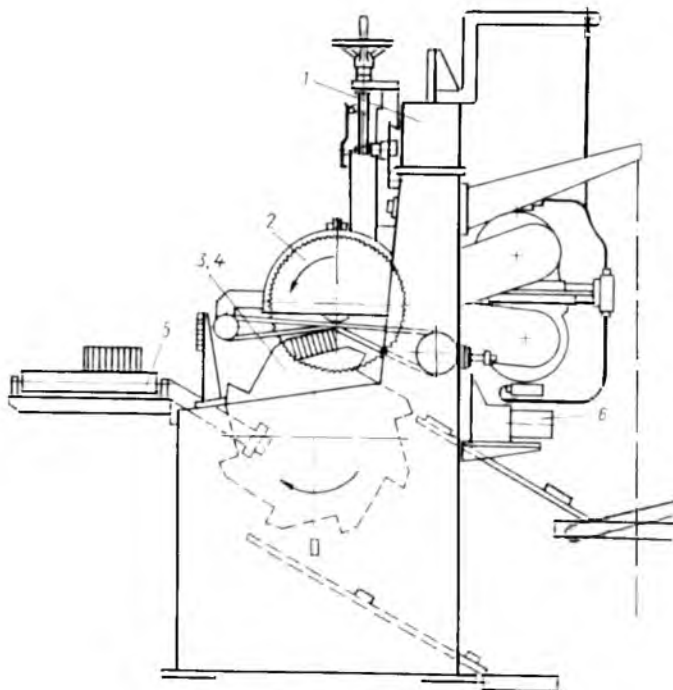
Схема восьмипильного торцового станка ГСПР16-М8:
